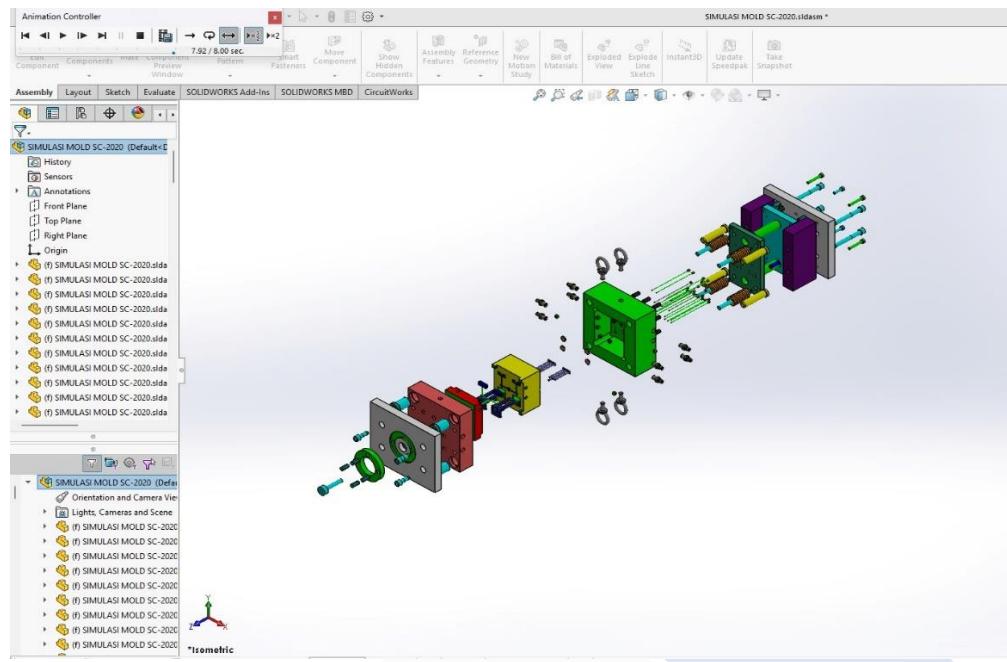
Proses Assembly Desain Cetakan Produk Holder
